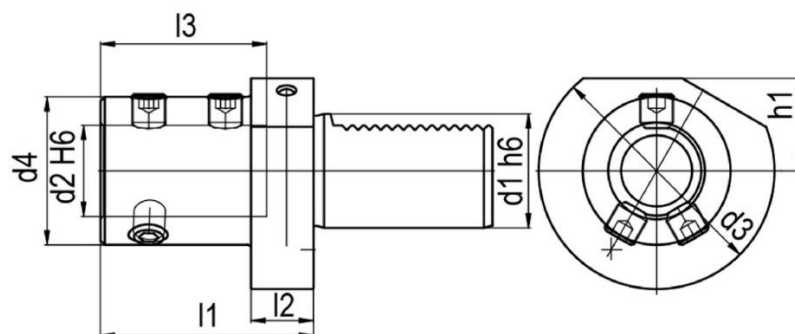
Оправка VDI40 для інструменту з хвостовиком типу Weldon E1-40x25
